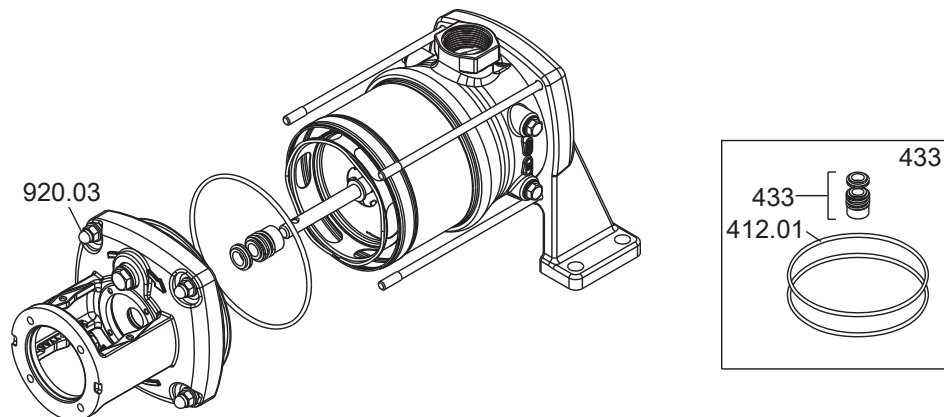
Gleitringdichtung ausbauen (Beispielzeichnung)
